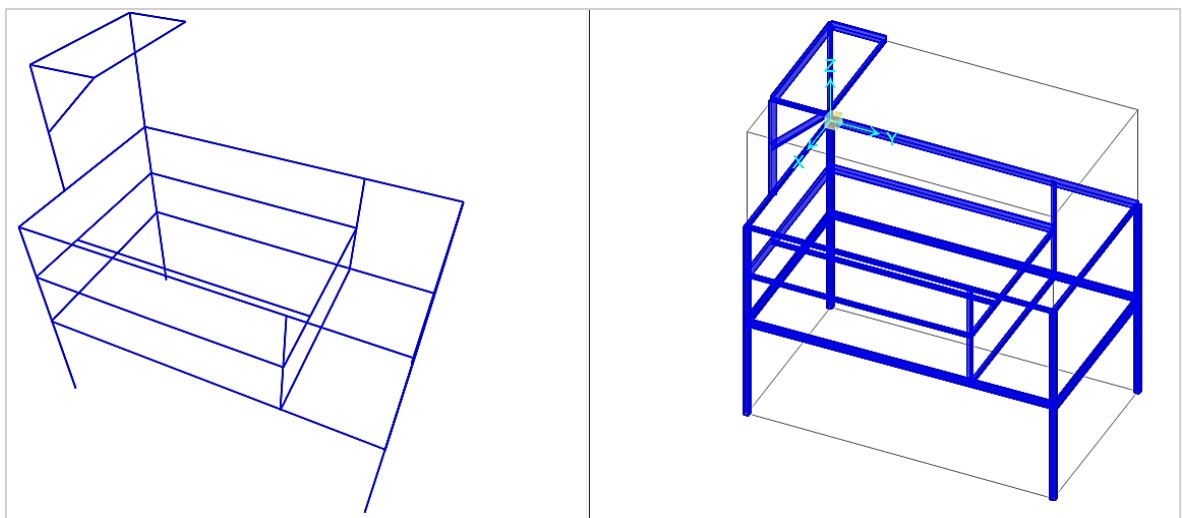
Diseño geométrico a) Diseño 2D, b) Diseño 3D
